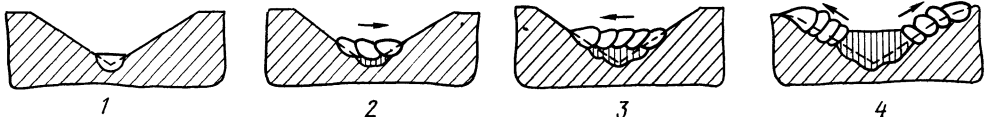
Последовательные стадии (1—4) наплавки ромбического калибра прокатного валка
